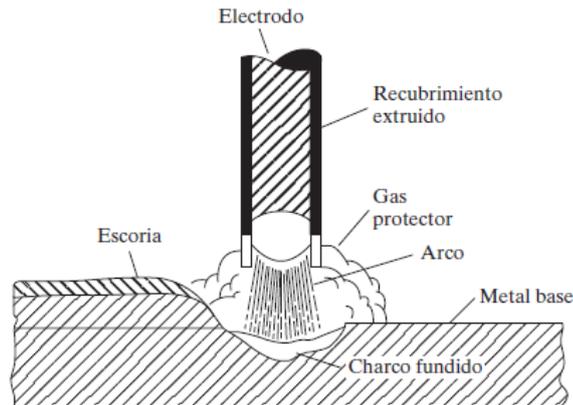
Elementos del proceso de soldadura de arco metálico protegido (SMAW). Fuente:[18].
